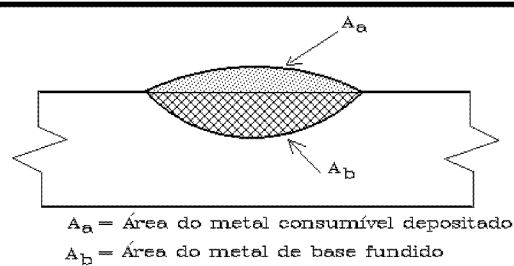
Seção Transversal do Metal de Solda, composta pelos Metais de Adição e Base.
